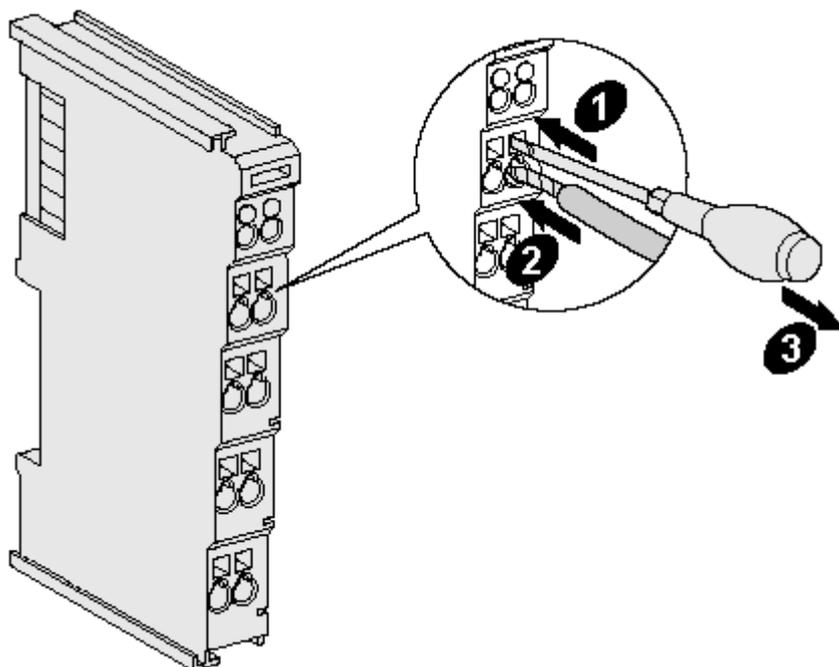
Befestigung einer Leitung an einem Klemmenanschluss
